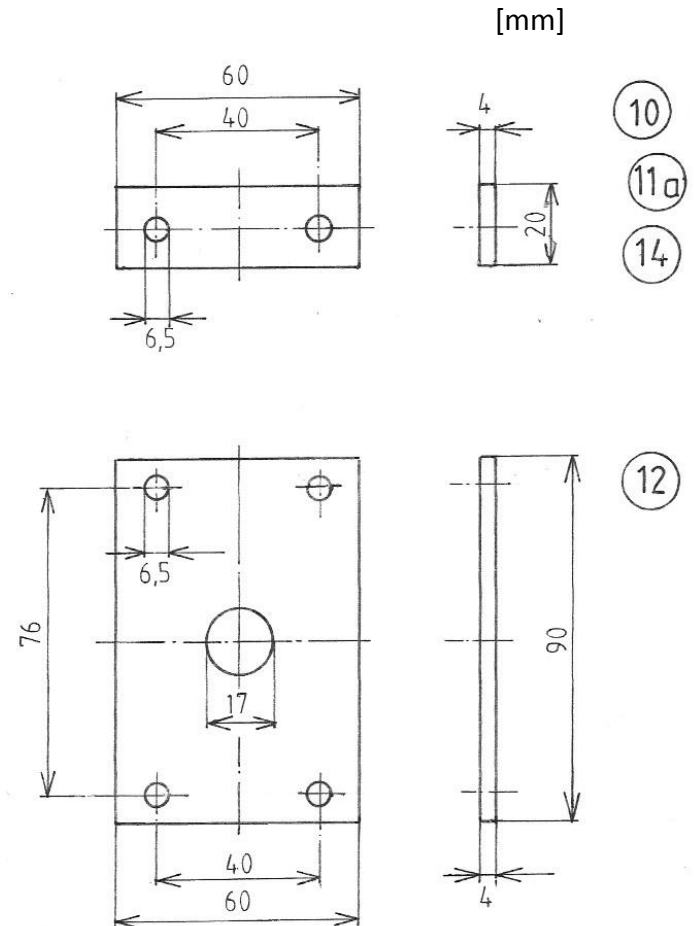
Sujetador del eje (10); sujetador de la placa de cojinete (11a);
